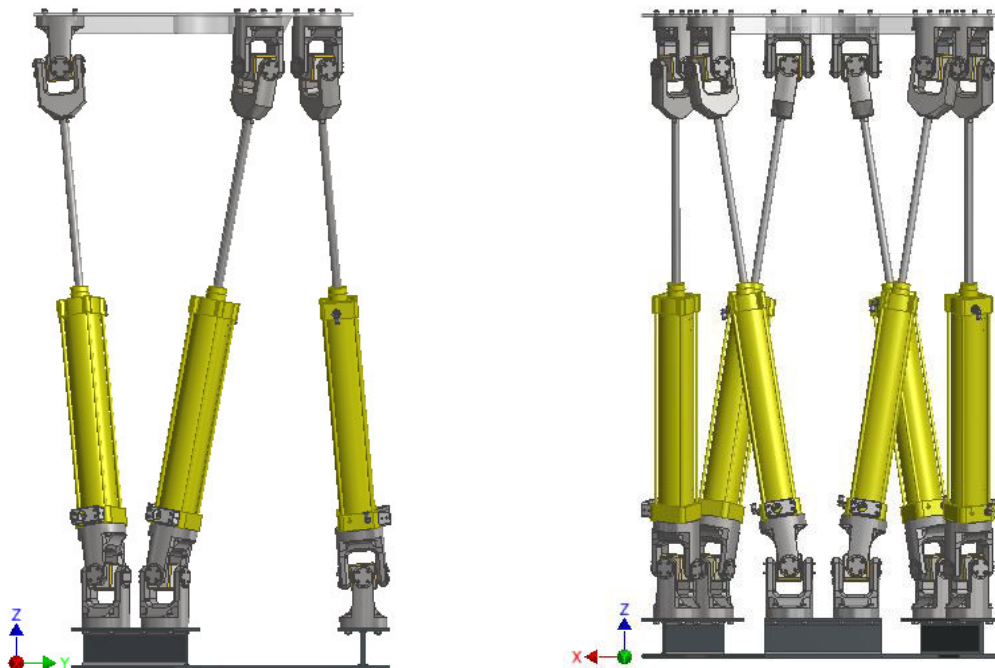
Desplazamiento en el eje Z de la plataforma Stewart-Gough (Vista de plano YZ y XZ)
